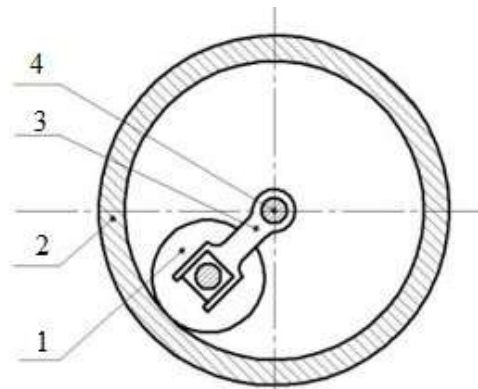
Конструкція повідково-планетарного віброзбудника коливань
